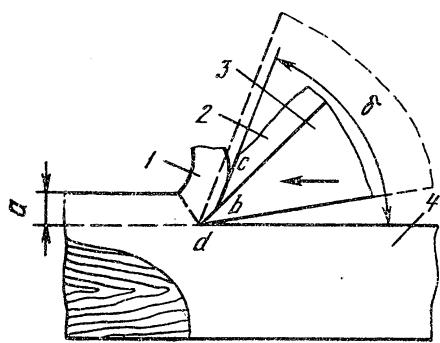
Схема строгания с продольной усадкой стружки шлифтиком:
